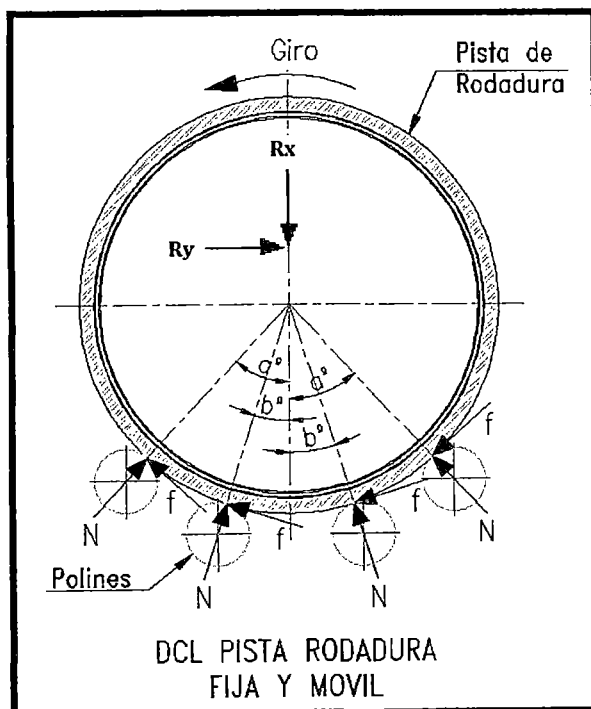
Fuerzas actuantes en las Pistas de Rodadura
